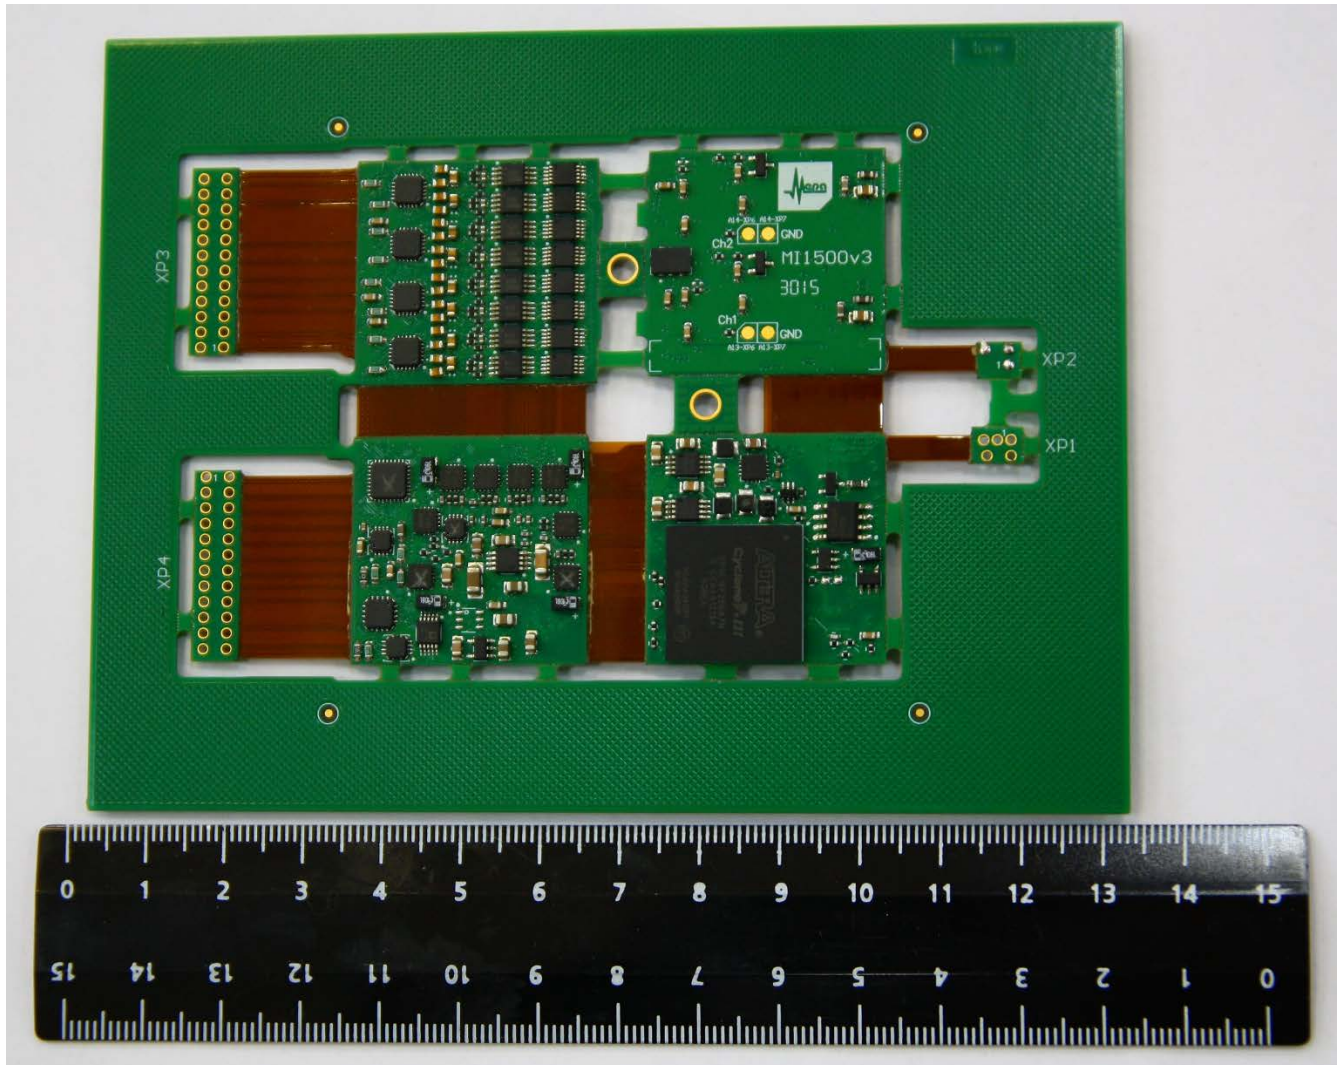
Внешний вид заготовки печатной платы Модуля измерения и передачи данных MI-1500.
